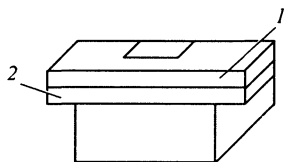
Второй этап цикла ВТО: 1 — боковая поверхность кожуха верхней подушки; 2 — боковая поверхность кожуха нижней подушки
